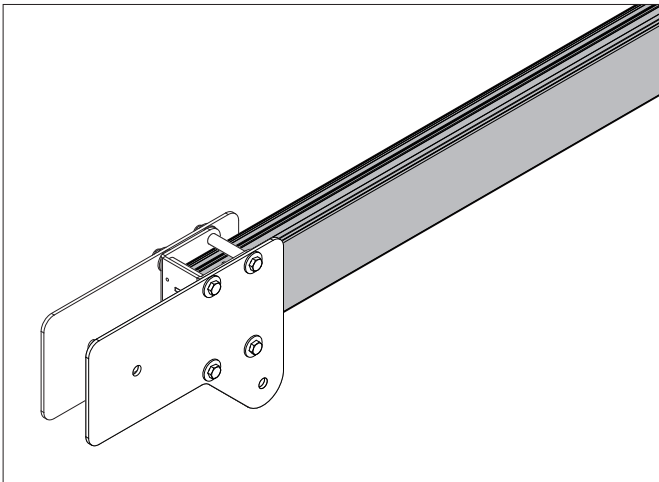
INSTALLAZIONE ASTA FISSA / FIX BAR INSTALLATION
